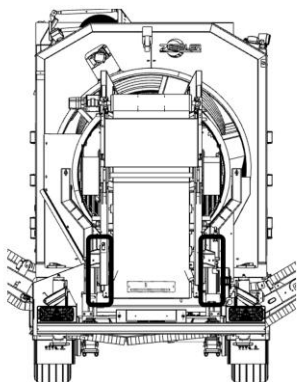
Positie hydraulische cilinder fijne fractie (1-B)
